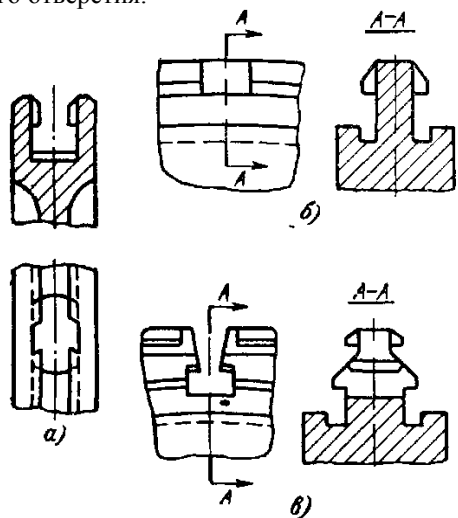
Наборка лопаток с излишним натягом. а—расклинивание щек хвоста лопатки, б — расклинивание щек обода диска.
